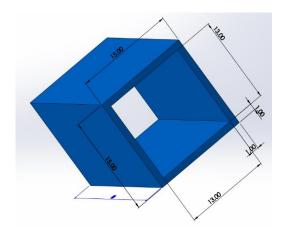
3^{\text{eme}}$ dimensionnement de la poutre
